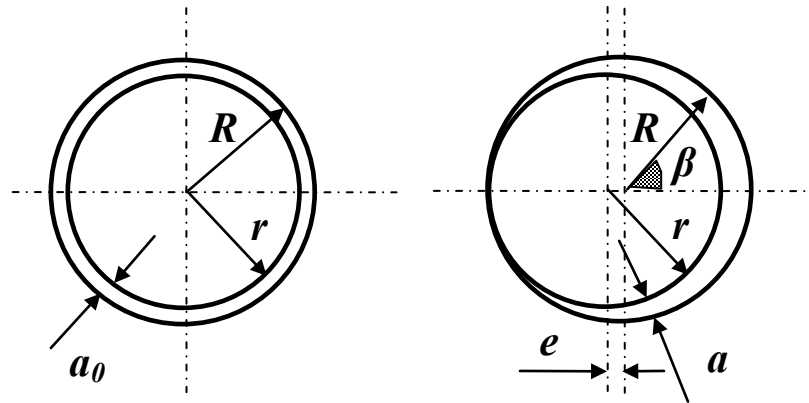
Розрахункова схема кільцевого зазора
